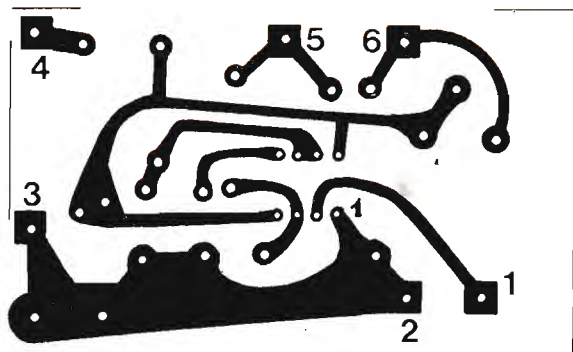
Disegno del circuito che il lettore dovrà riprodurre su una basetta di materiale isolante e nelle stesse dimensioni ricavate da questa figura.
